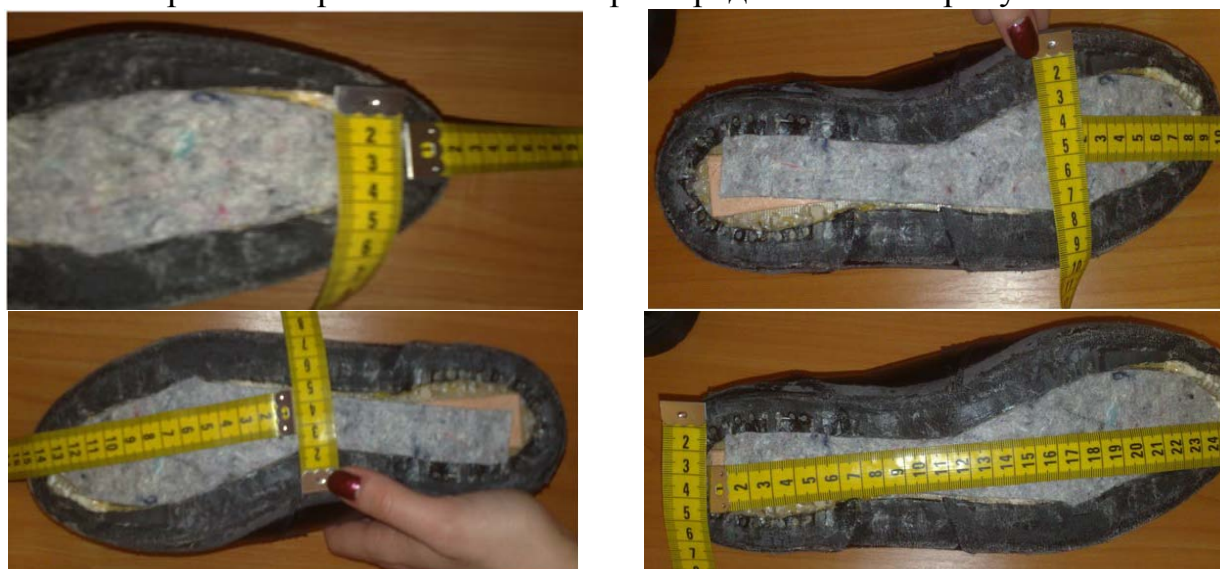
Измерение ширины заготовки верха полуботинок в четырех точках
